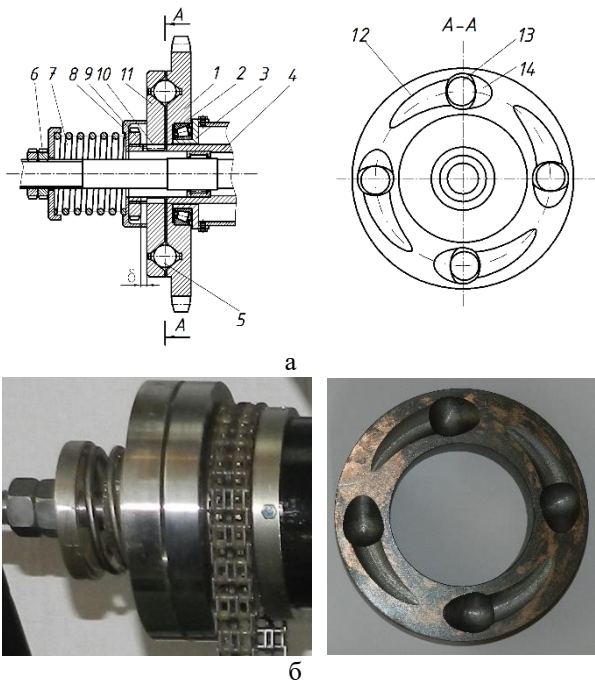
Конструктивна схема (а) та загальний вигляд (б) запобіжної муфти і робочої поверхні веденої півмуфти: 1 – ведуча півмуфта; 2 – радіально-упорний підшипник; 3 – корпус; 4 – вал шнека; 5 – кульки; 6 – гайка; 7 – центральна пружина; 8 – втулка; 9 – гайка; 10 – шліци; 11 – ведена півмуфта; 12 – похила робоча канавка; 13 – лунки; 14 – похила зворотна канавка.
